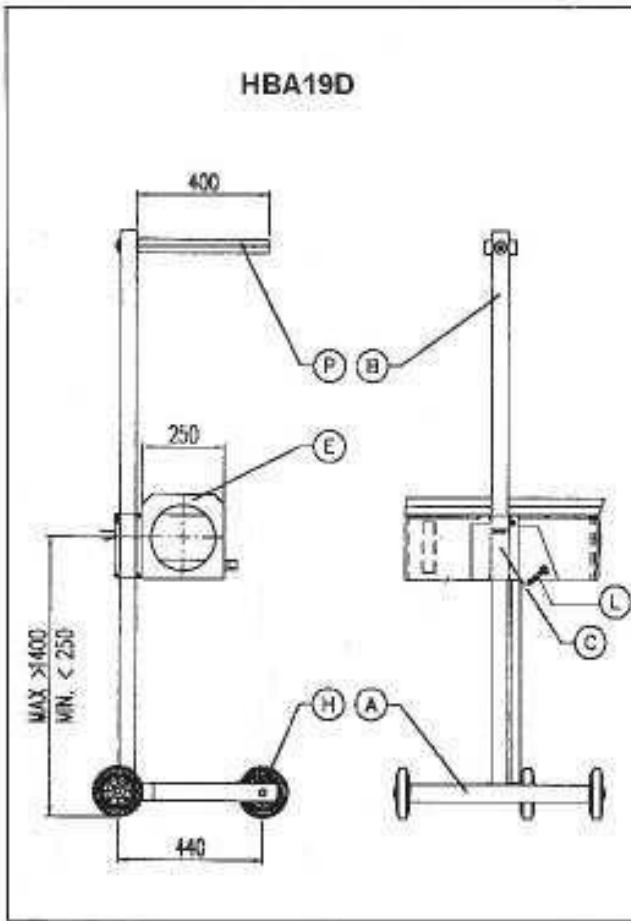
Montaggio - Mounting - Montage - Montage - Montaje - Montaje - Montage
